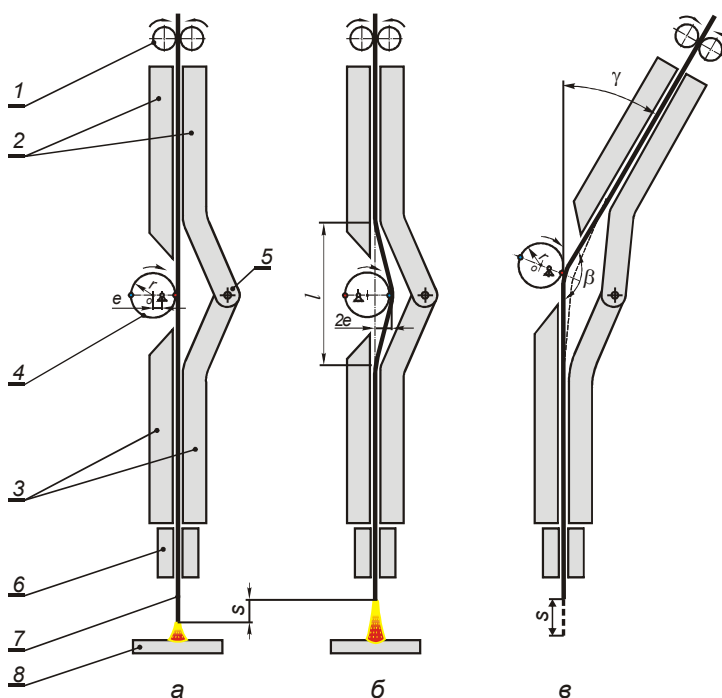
Схема устройства для принудительного механического переноса электродного металла: а, б – без начального изгиба ленточного электрода; в – с предварительным изгибом на угол β
